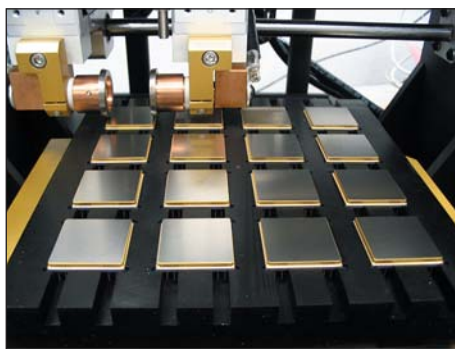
Групповая и одиночная шовно-роликовая сварка
